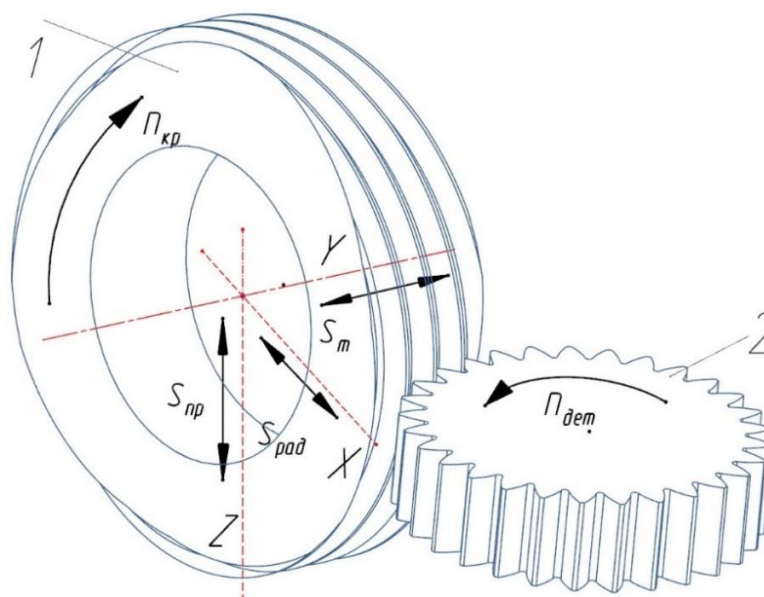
Схема обкатного непрерывного зубошлифования: 1 – червячный круг; 2 – зубчатое колесо
